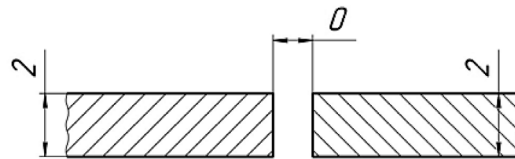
Конструктивні елементи деталей з'єднання, підготовлені до зварювання
